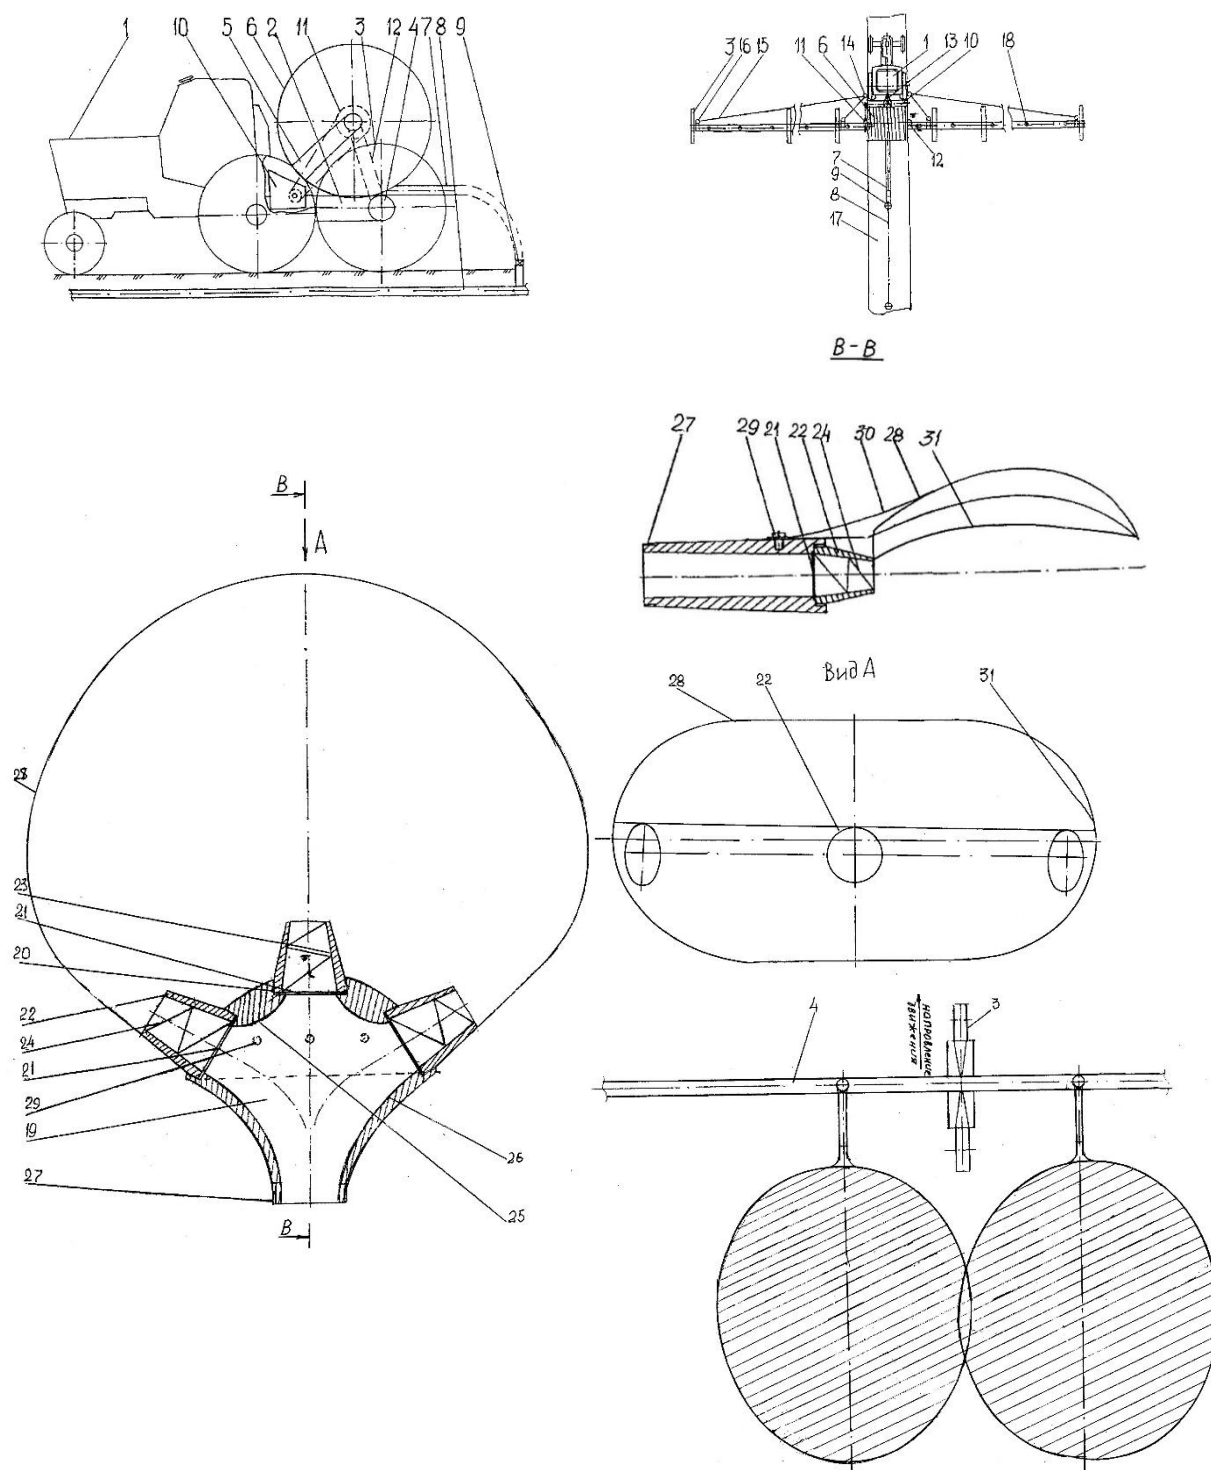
Колесный дождевальнй агрегат фронтального перемещения 1 – трактор; 2 - опорная рама; 3 - опорные колеса; 4 - напорный трубопровод; 5 - кронштейны; 6 – барабан; 7 - гибкий напорный трубопровод; 8 - закрытый напорный трубопровод; 9 – гидрант; 10 –редуктор; 11 - цепная передача; 12 - патрубок; 13 - сцепное устройство; 14 – стойки; 15 – растяжки; 16 – кронштейны; 17 - технологическая дорога; 18 - поворотные дождеватели; 19 - расширительная камера; 20 -резьба; 21 - герметизирующие прокладки; 22 - стволы-жиклеры; 23 - Внутренняя полость; 24 - сменные спиральные направляющие; 25 - сферические направляющие; 26 - внутренняя часть стенки; 27 - входной патрубок; 28 - формирователь зоны дождя; 29 – винты; 30 - ребро жесткости; 31 - боковые направляющие стенки.
